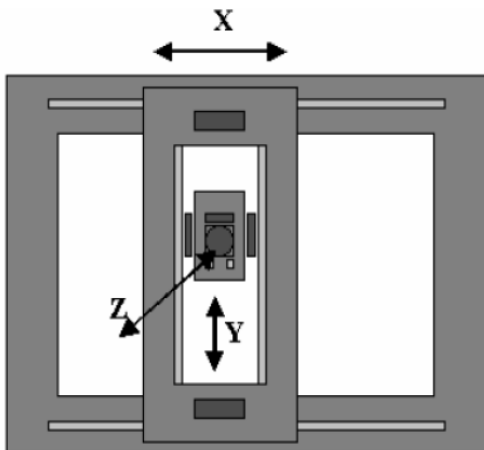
Компоновка обробного центру з 3-ма ЛД. Кольором позначено: механічна система; лінійні напрямні; ЛД.
